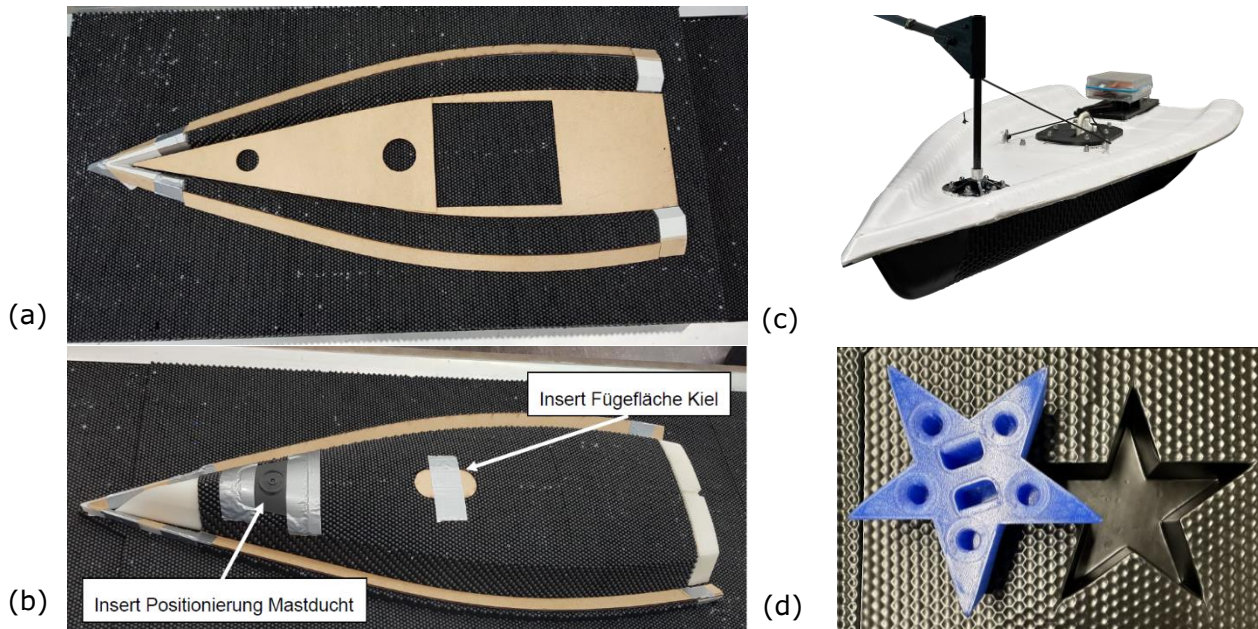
Werkzeugformen für Bootshälften mit Inserts für Klebeflächen [6]
